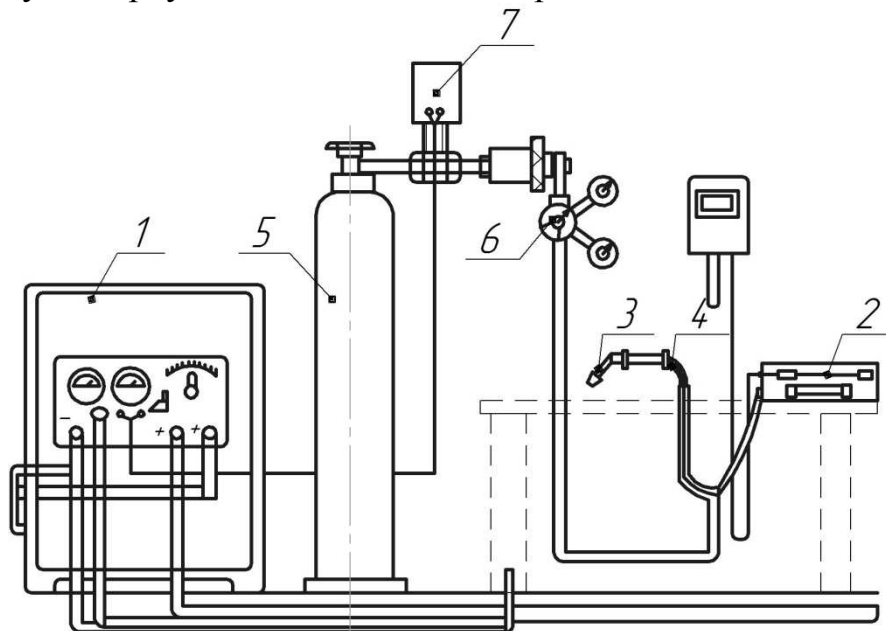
Схема полуавтомата для сварки в углекислом газе:
